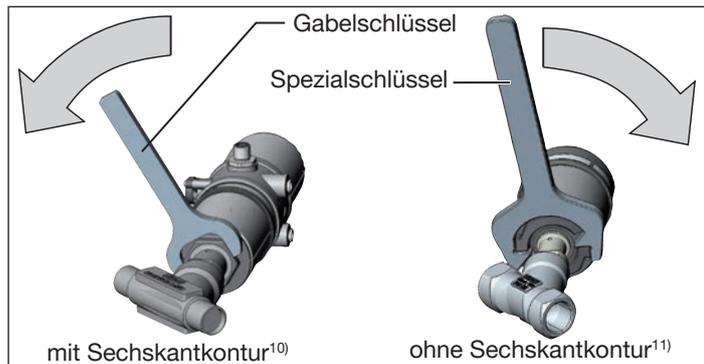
Drehen mit Gabelschlüssel / Spezialschlüssel
